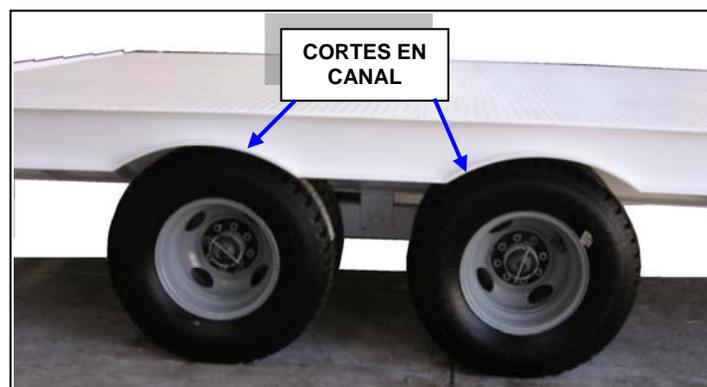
Detalle de cortes para salpicaderas en canal lateral.
